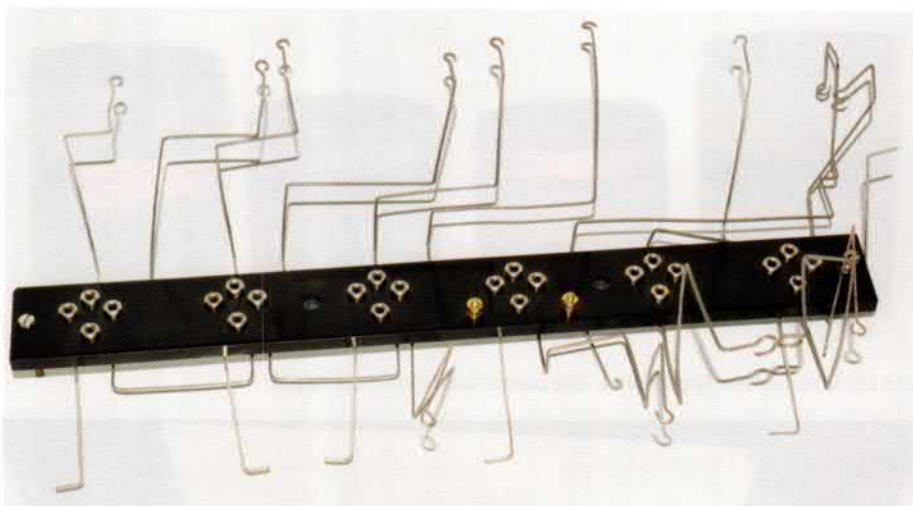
Röhrenfassungen mit Verdrahtung vor dem Einbau
